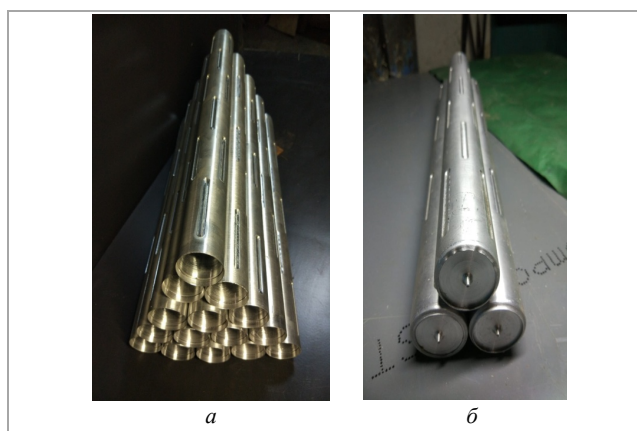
Фото обечаек (а) и корпусных устройств в сборе (б)
